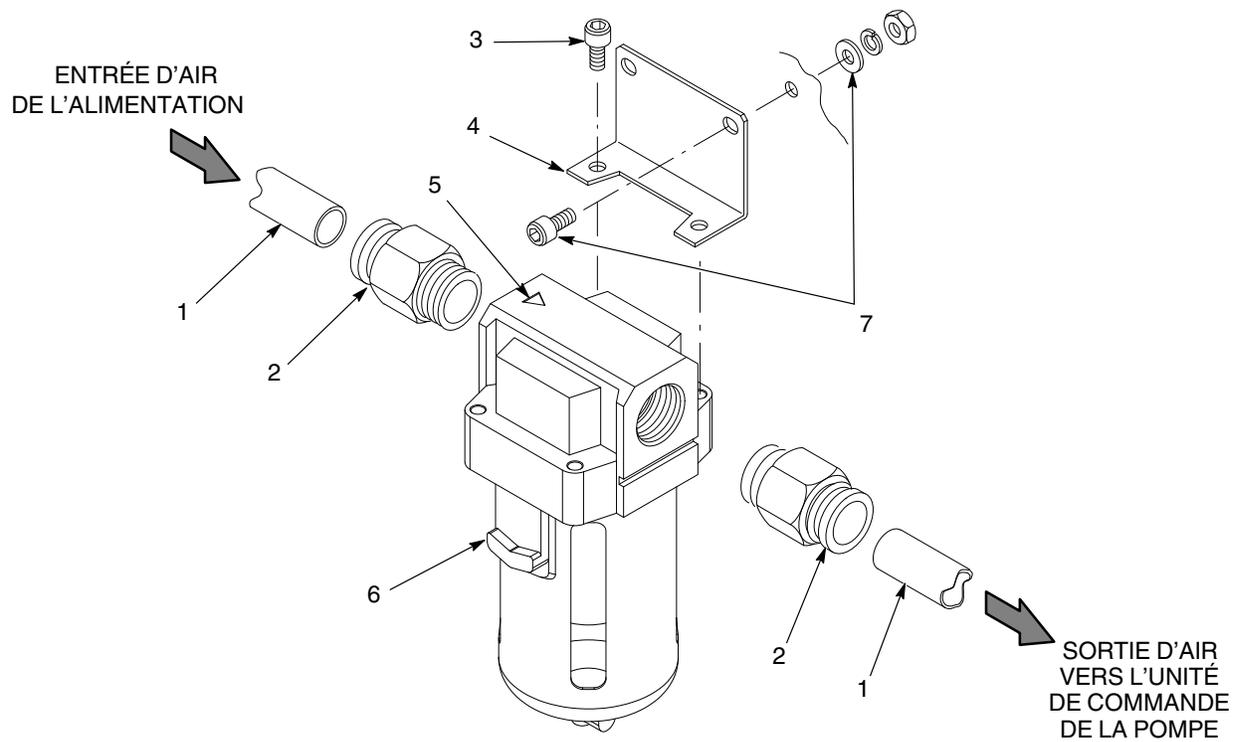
Installation du filtre à air – Systèmes autonomes et à montage sur rail/mural
